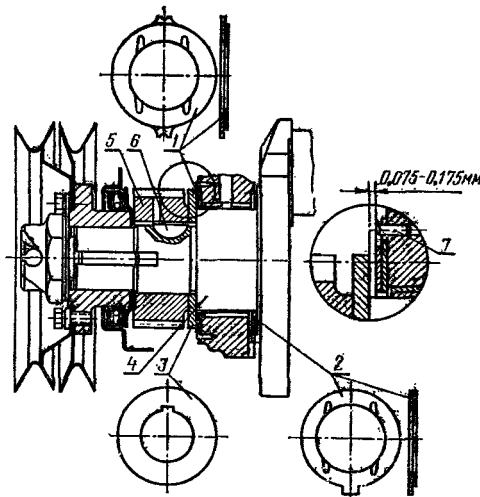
Первый коренной подшипник коленчатого вала двигателей ГАЗ-52:
